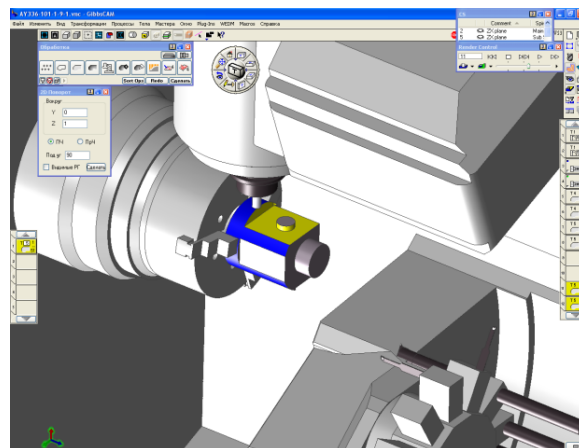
Выполнение обработки фрезерным мотор – шпинделем
